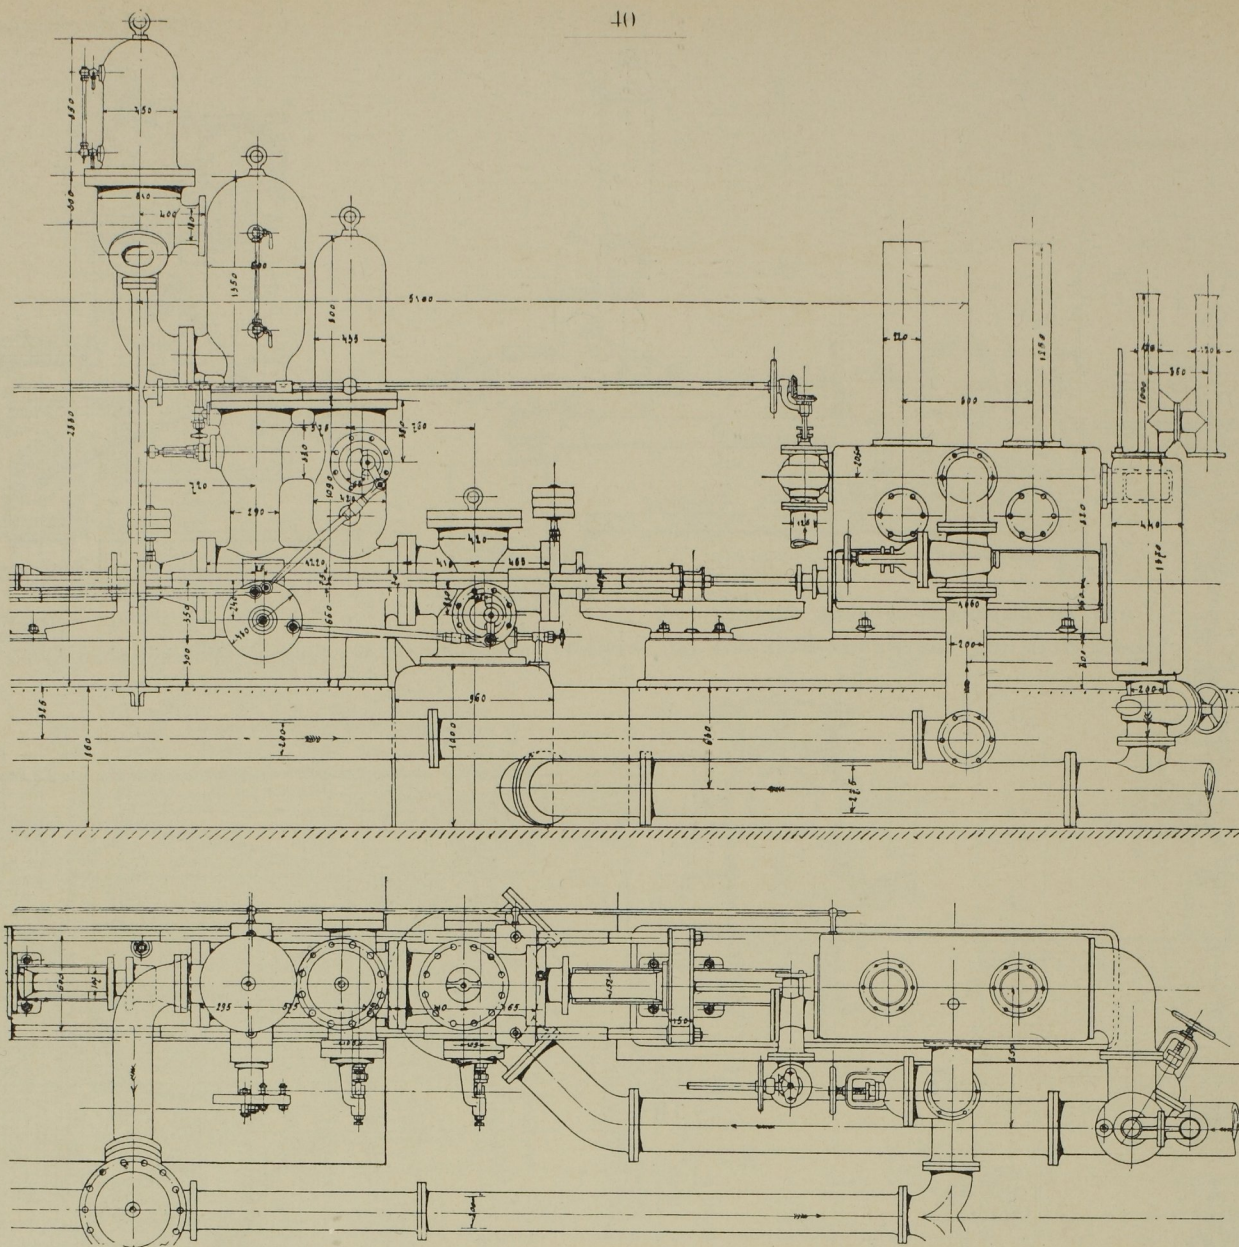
Seitenansicht und Grundriss einer Maschinenhälfte. Massst. 1 : 45.
